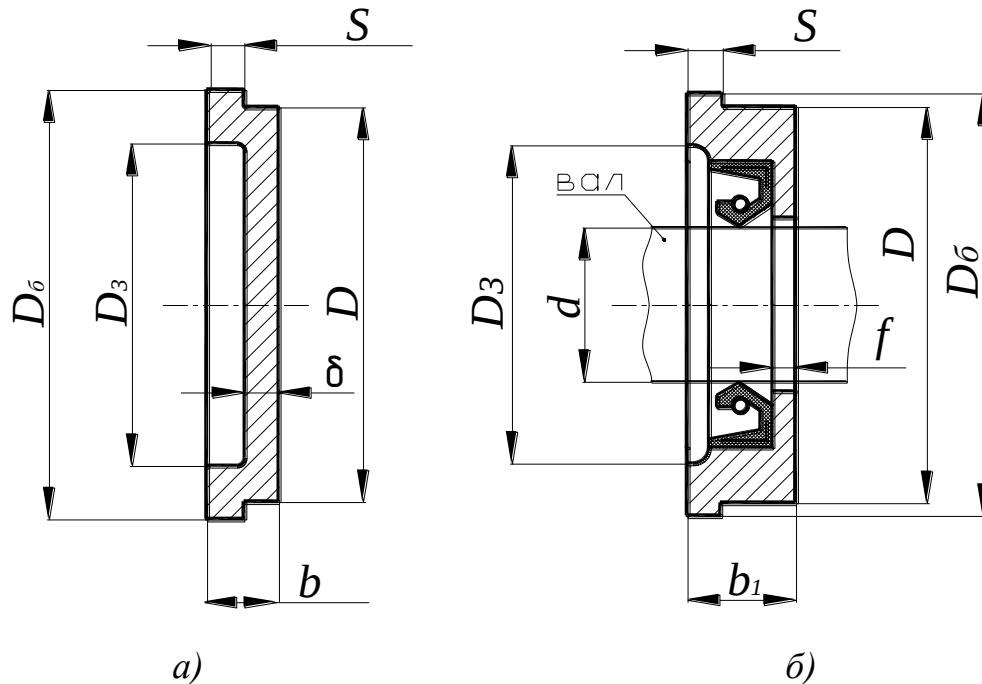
Крышки подшипниковых узлов: а) глухая; б) сквозная.
